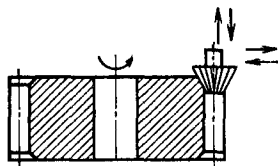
Схема снятия фаски на торцевых кромках зубьев колеса конусной фрезой
